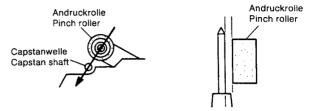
Parallelität der Andruckrolle - 2 Fig. 3-20 Pinch roller parallel - 2
